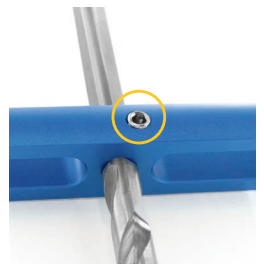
Gewindestift lösen, um den Bohrer zu verschieben.
